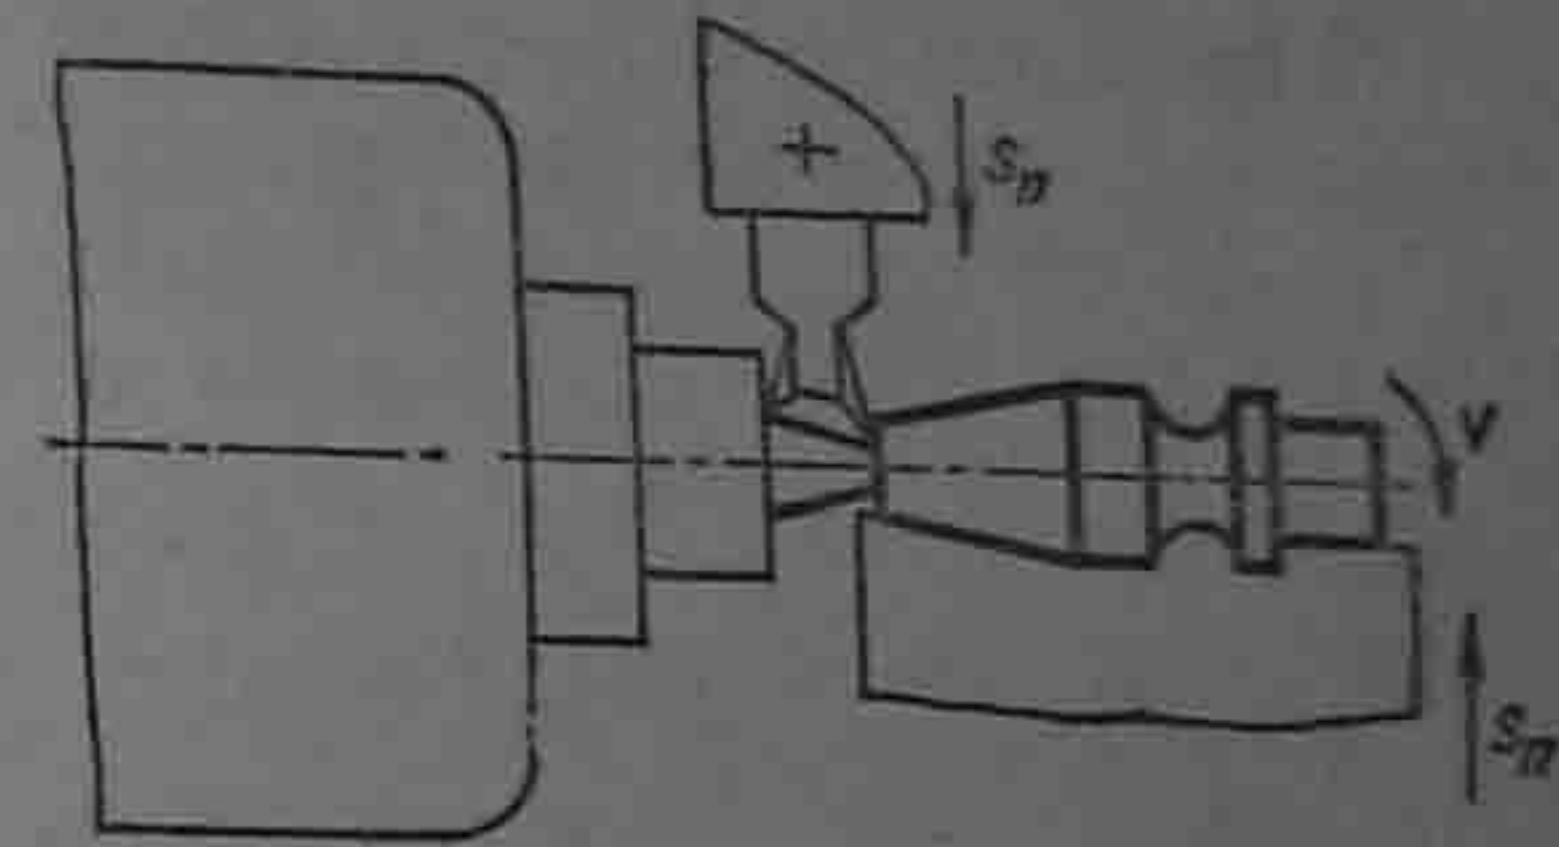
Схема обработки заготовки на токарном одношпиндельном фасонно-отрезном автомате
